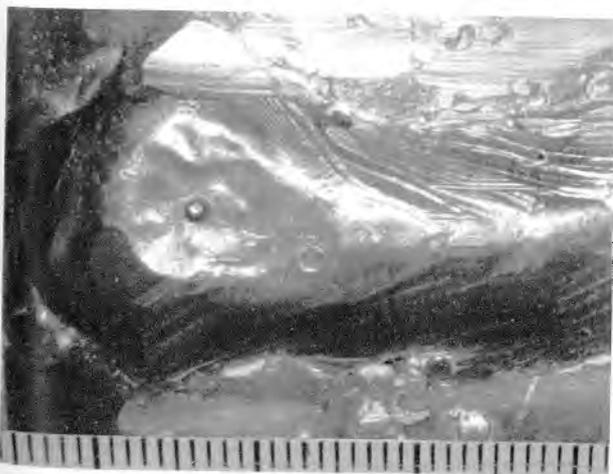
Кратер 1 с небольшим металлическим включением 2 в стыковом сварном соединении строительной конструкции
